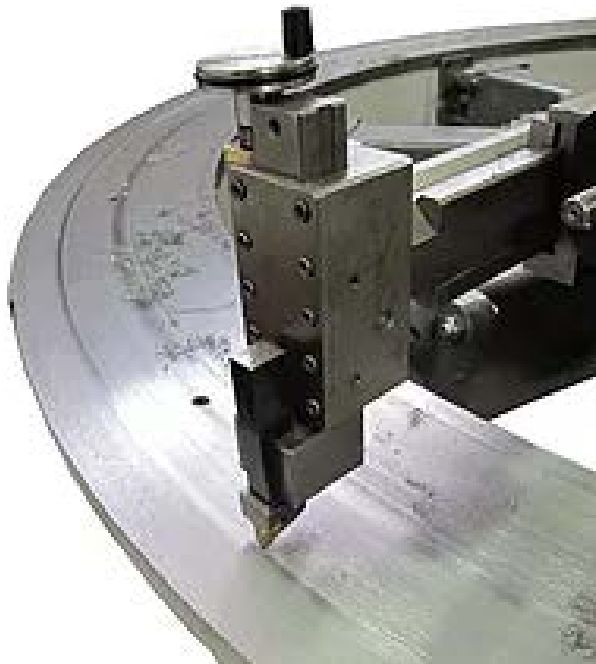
Мобільний металорізальний агрегатний верстат FFMM-4000
